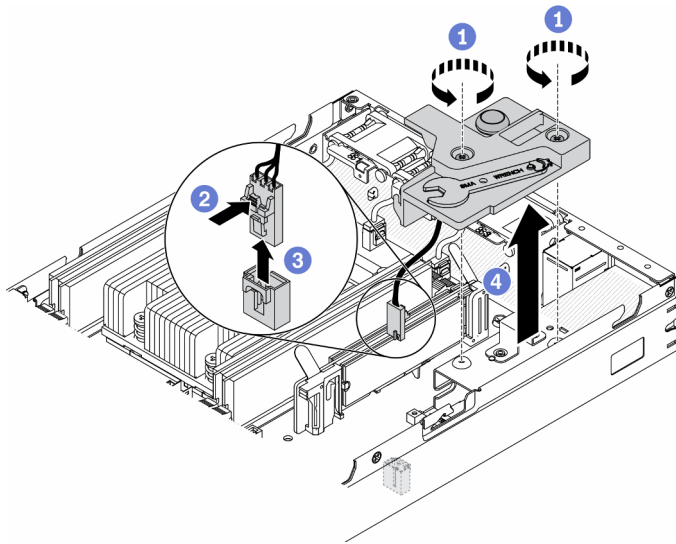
Entfernen des Kabels für den Schalter gegen unbefugten Zugriff
